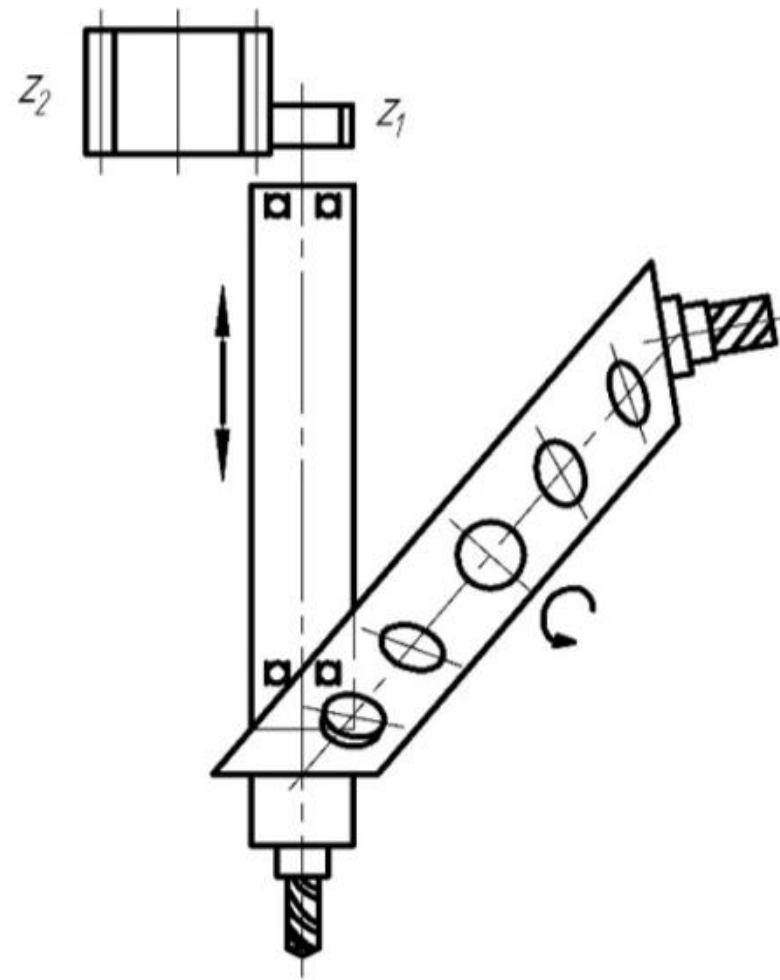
ПАЗІ з використанням револьверної головки для розширення набору інструментальних оправок
